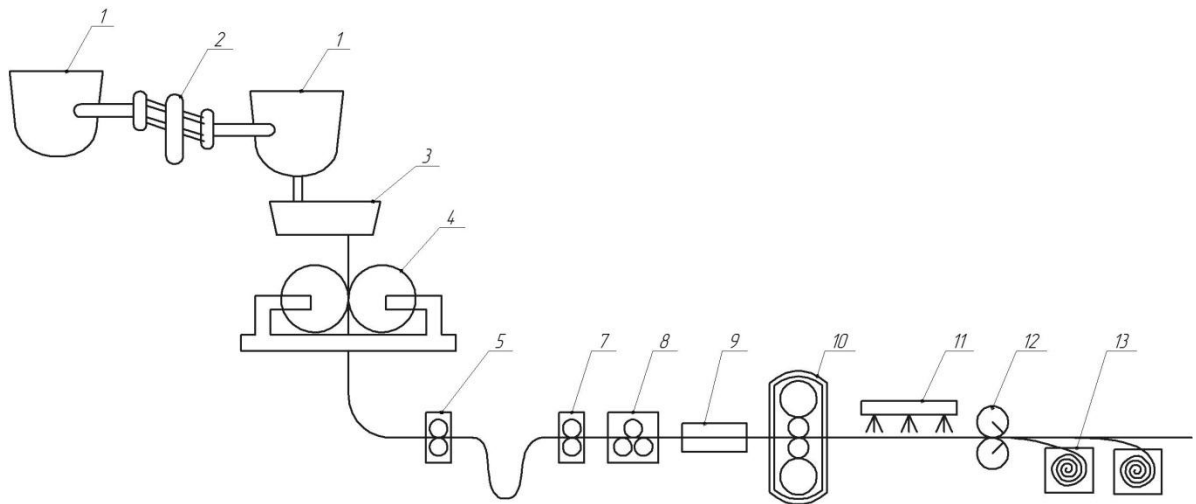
Схема розташування обладнання промислового двовалкового ливарно-прокатного модуля для виробництва тонкої сталеві смуги в Крефельді (Німеччина) [2]: 1 – розливні ковші; 2 – повертальний стенд; 3 – проміжний ківш; 4 – ливарно-прокатна машина; 5 – тягнучі ролики; 6 – петленакопич; 7 – спрямовуючі ролики; 8 – трироликівий блок; 9 – індукційний підігрівач; 10 – прокатна кліть; 11 – дільниця ламінарного охолодження; 12 – ножиці; 13 – моталки
